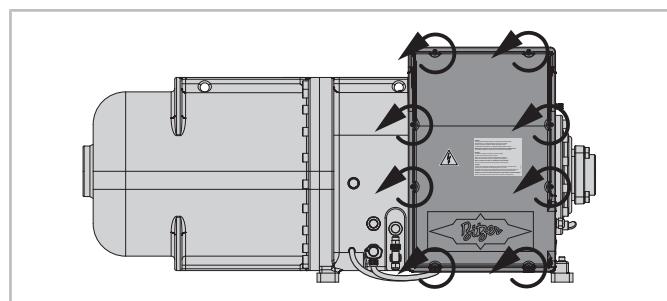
CSV.2: Снятие крышки корпуса FI.
